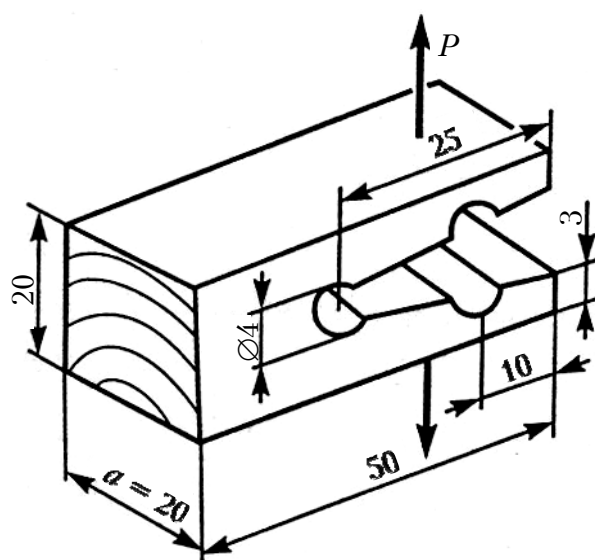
Форма и размеры образца для испытания древесины на раскалывание
